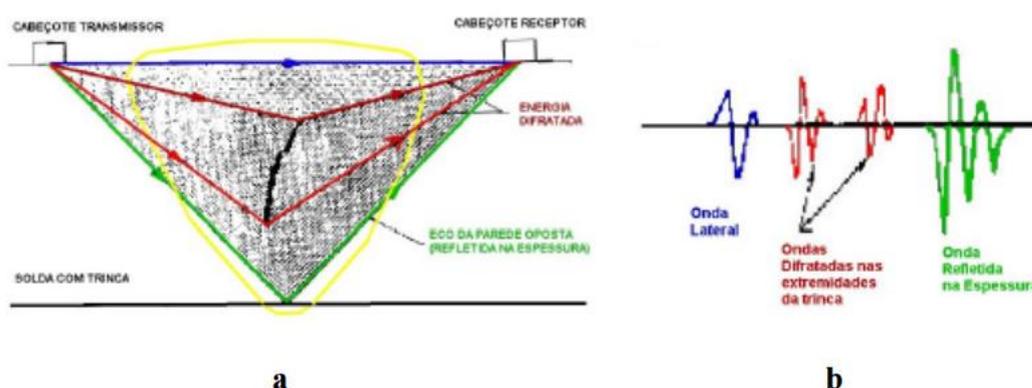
Princípios da técnica TOFD na inspeção de solda, formação dos sinais.
